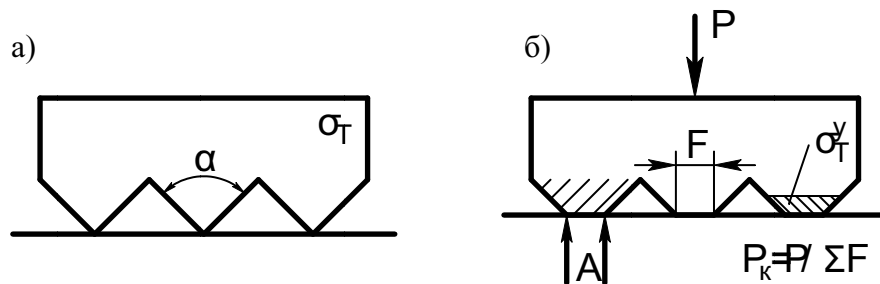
Схема образования физического контакта: а – до сварки; б – при сварке
